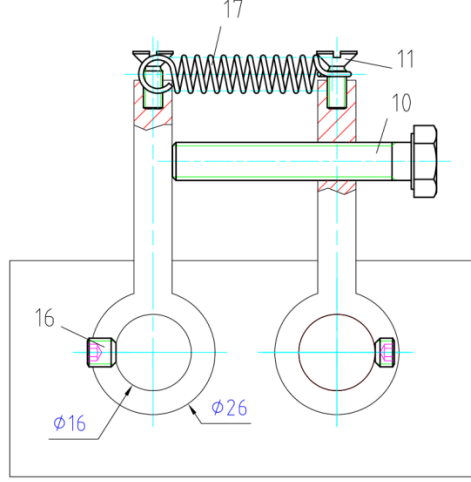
'de iplik tutucu mekanizmanın ana gövdeye montaj şeması görülmektedir.
